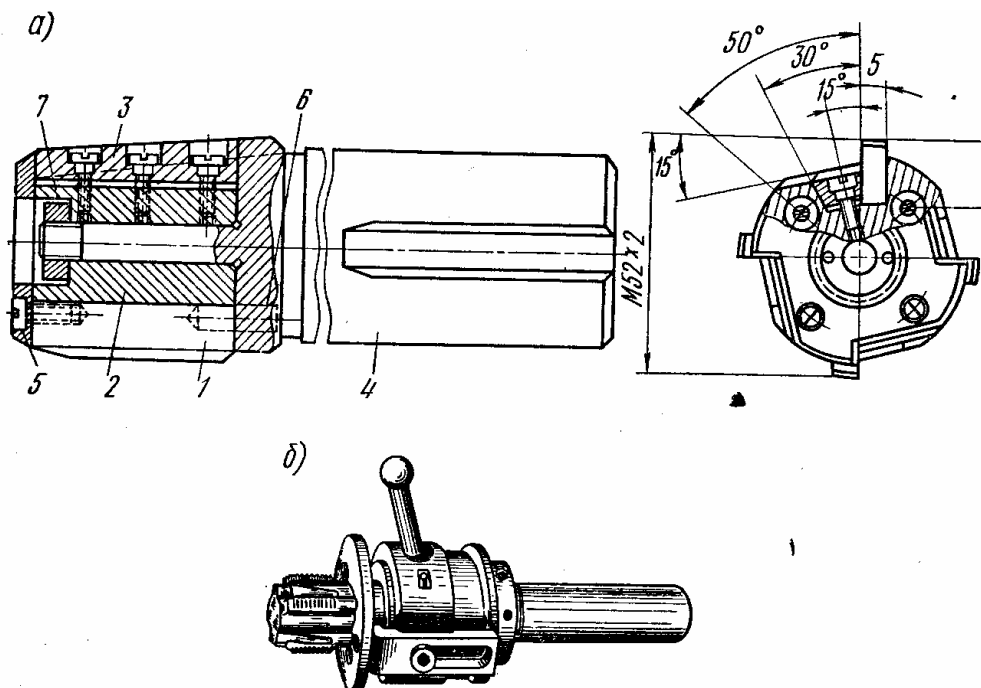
Сборный метчик (*а*), резьбонарезная головка для нарезания внутренней резьбы (*б*)
